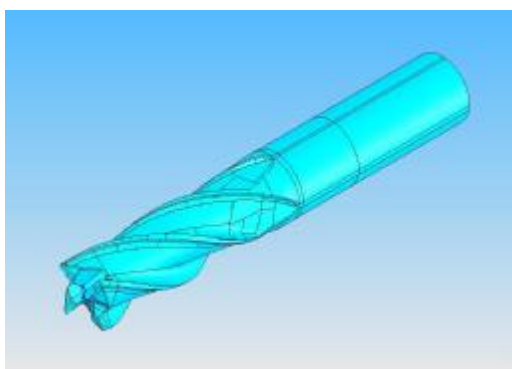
Výsledný STL soubor, detail špičky zubu.
